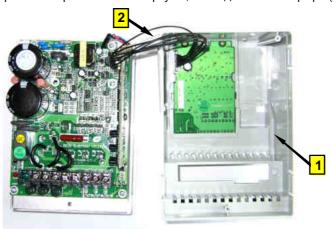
1 – верхняя часть корпу са; 2 – шлейф ЦП.
